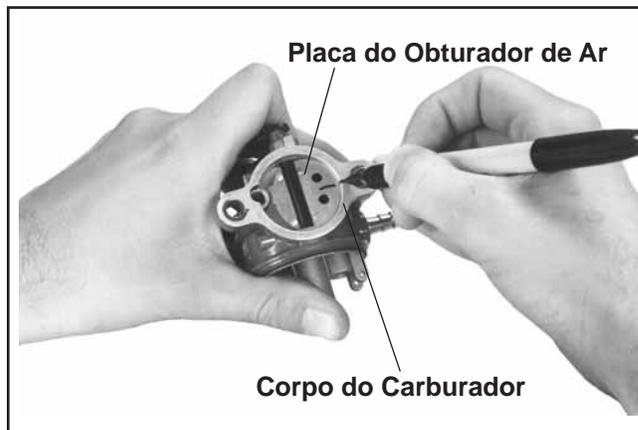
Marcar a Placa do Obturador de Ar e o Corpo do Carburador.
